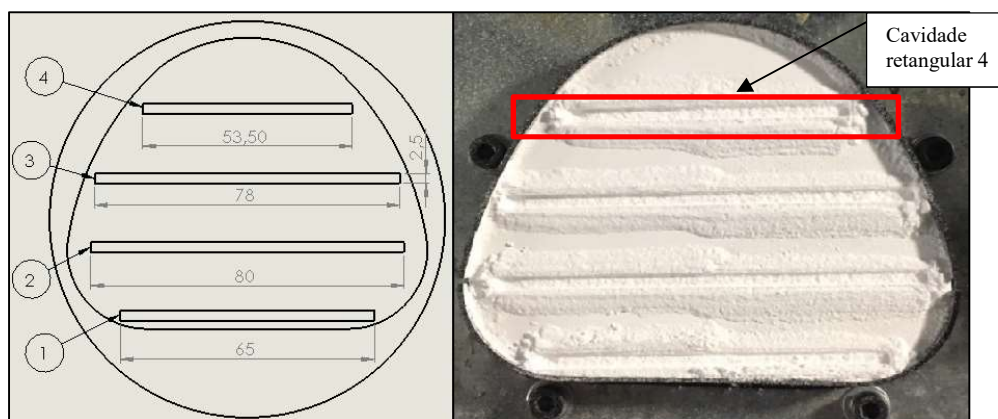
Sequência de usinagem e dimensões em milímetros (esquerda), bolsas retangulares usinadas (direita).
